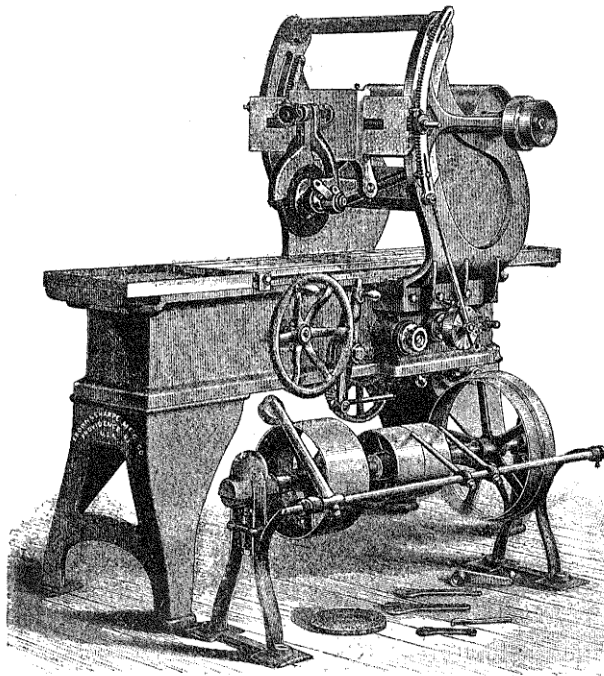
Machine Brown et Sharpe à rectifier les surfaces planes.
